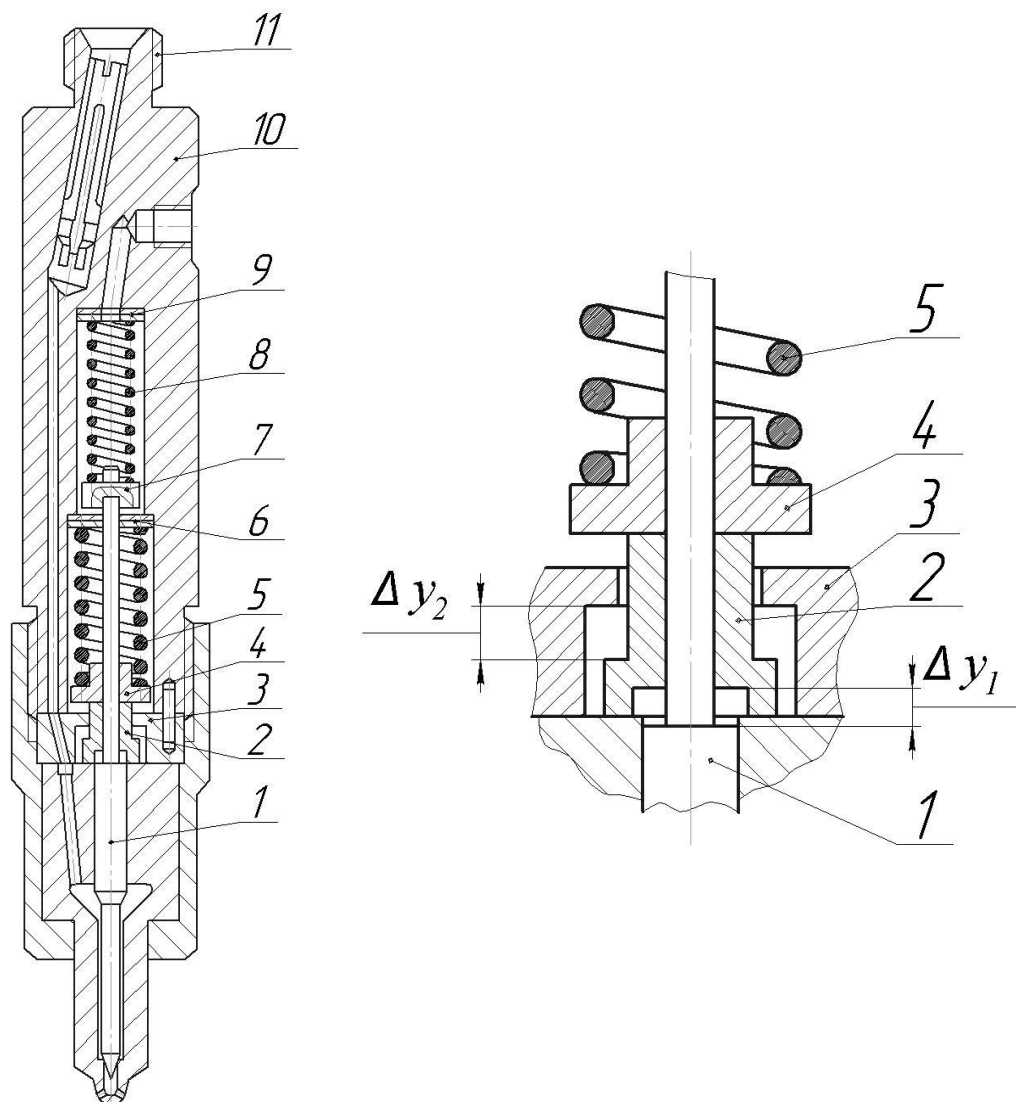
Форсунка механическая со ступенчатой характеристикой впрыска топлива: 1 – игла распылителя с удлиненным штоком; 2 – втулка с проточкой; 3 – проставка; 4, 7 – тарелки пружин; 5 – пружина; 6, 9 – регулировочные прокладки; 10 – корпус форсунки; 11 – штуцер
